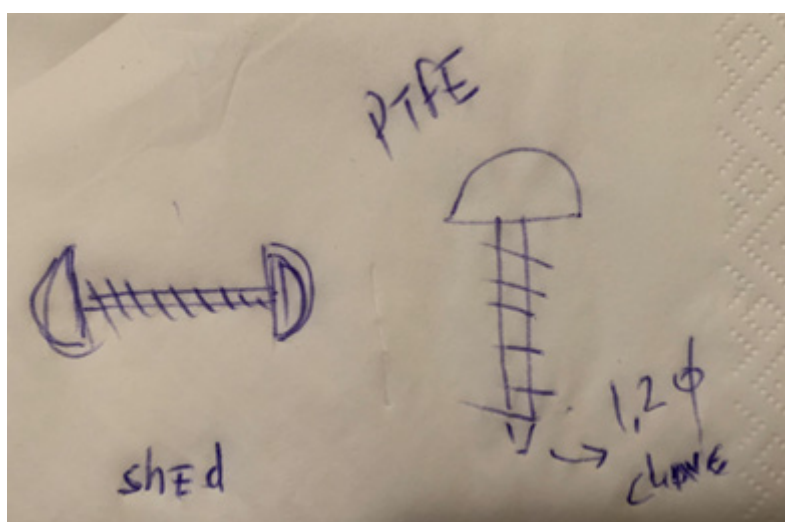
Primeiro esboço do projeto da Barbell Technique®
